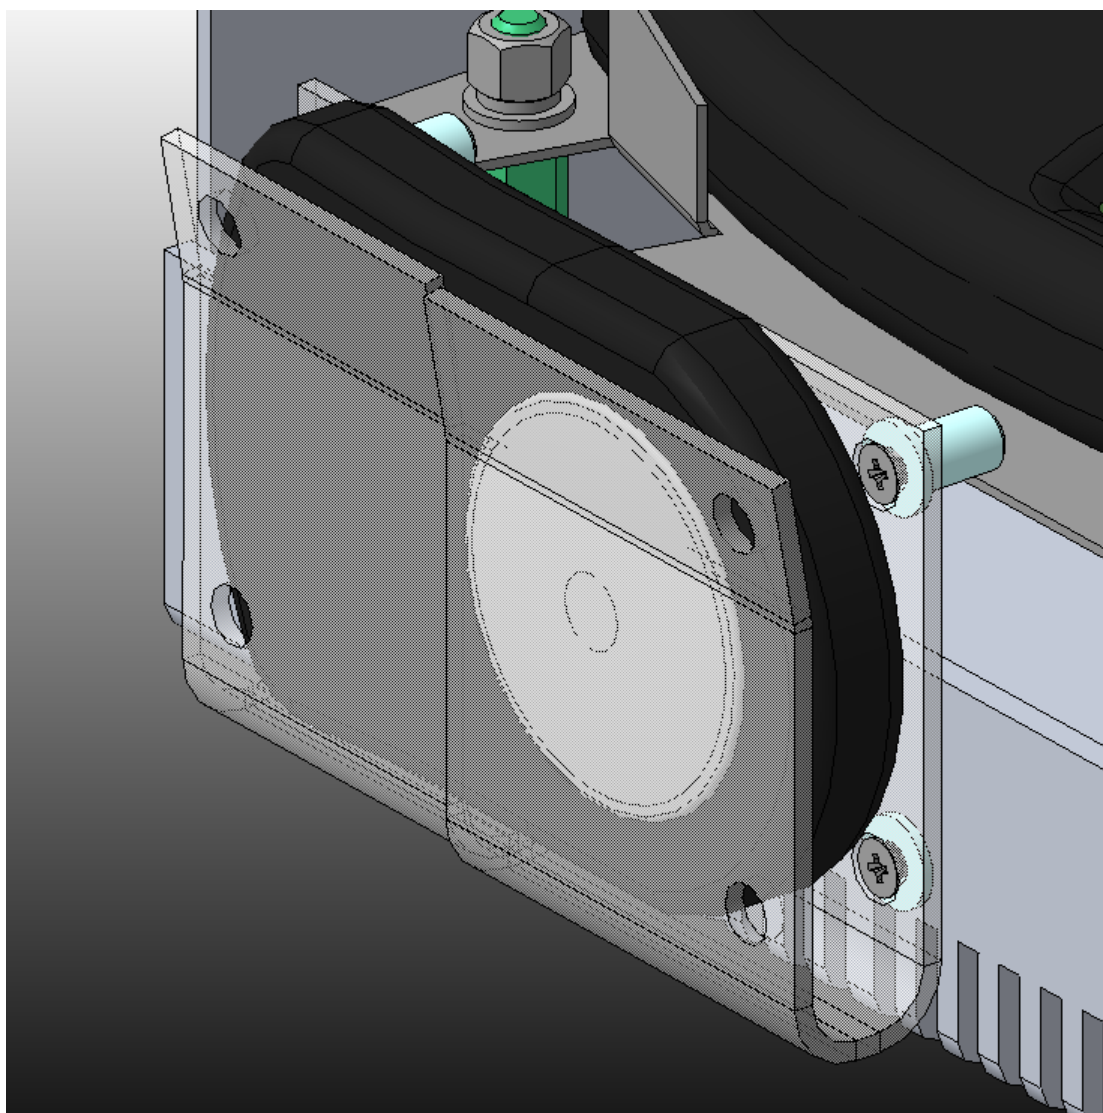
Крепление держателя головки люксметра к корпусу стенда (крышка корпуса не показана).
